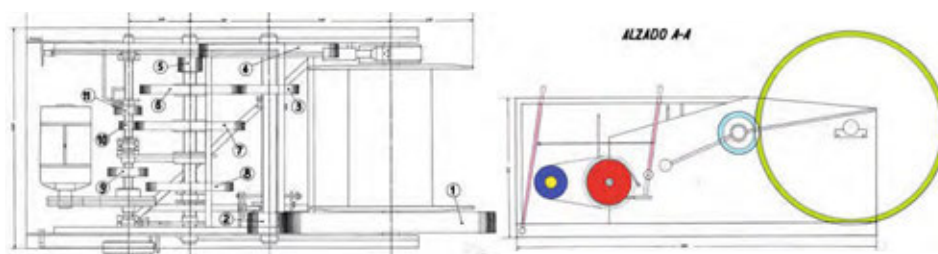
y 68. Planta y alzado de un cabrestante. AF. Plano E319.2. 10-X-51.
